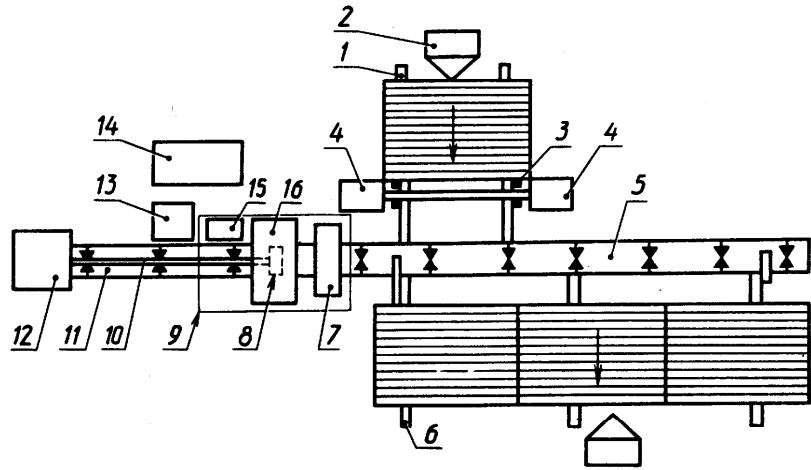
Схема трубосварочной базы с использованием установки контактной сварки типа ТКУС
